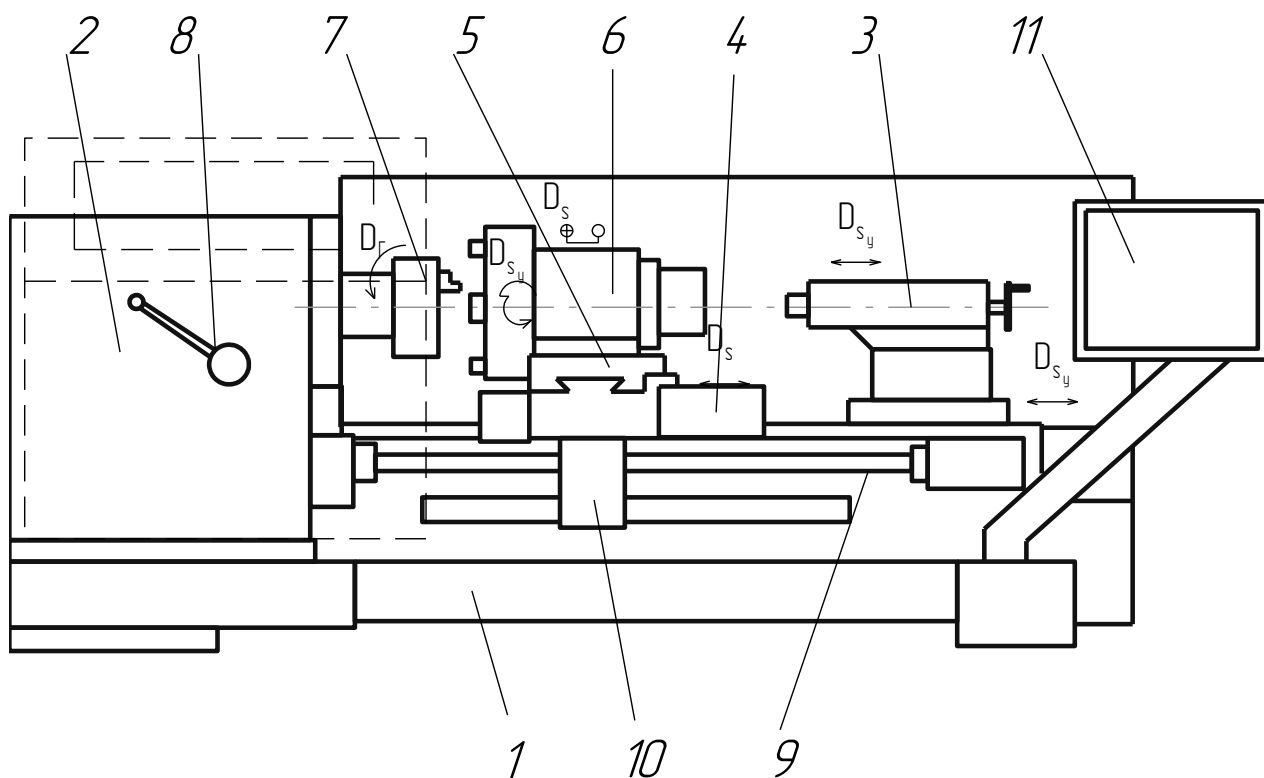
Схема токарного станка 16К20Ф3 NC201М
